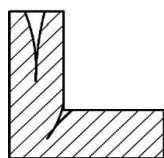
Дефект - газовая раковина: дефектная отливка
